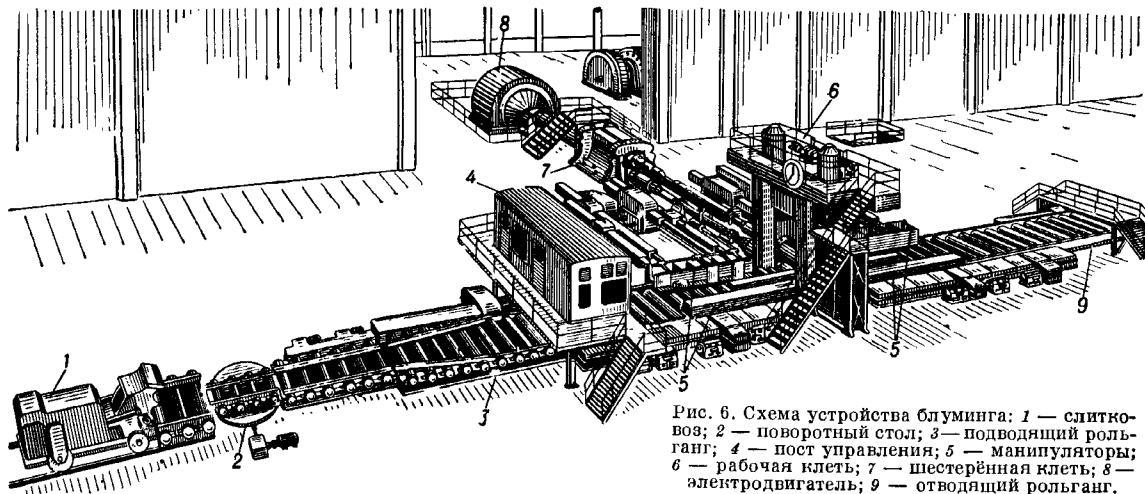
Схема устройства блюминга: 1 — слитковоз; 2 — поворотный стол; 3 — подводный ролик; 4 — пост управления; 5 — манипуляторы; 6 — рабочая клетка; 7 — шестерённая клетка; 8 — электродвигатель; 9 — отводящий ролик.
